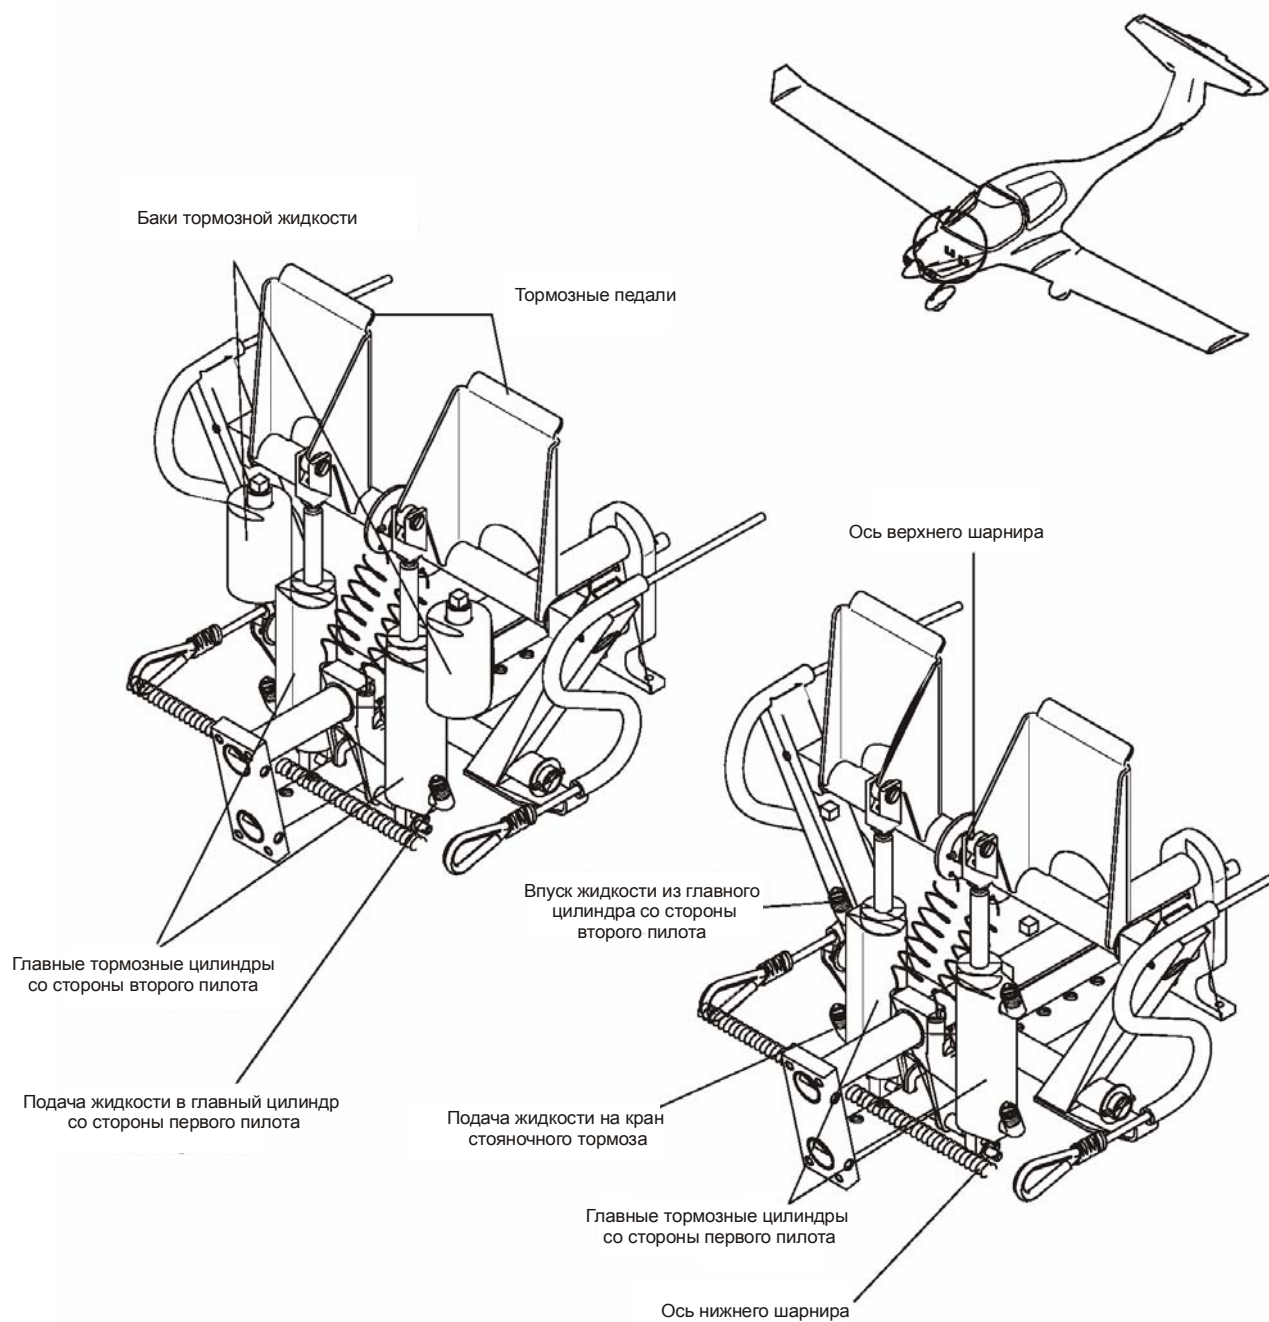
Установка главного тормозного цилиндра и бака тормозной жидкости
